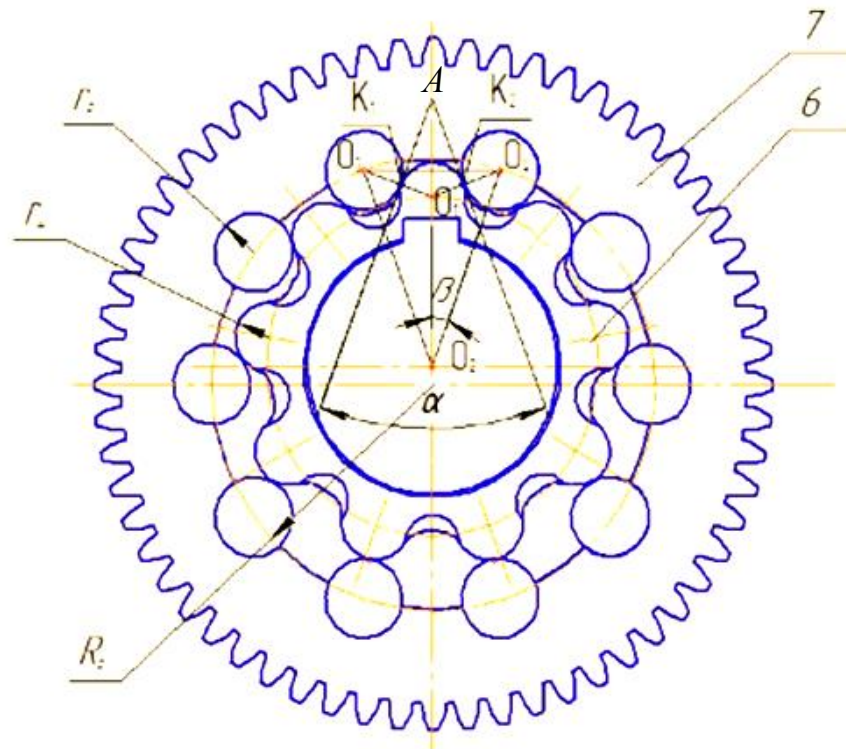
Розрахункова схема для визначення кута призми рухомої вимірювальної поверхні
